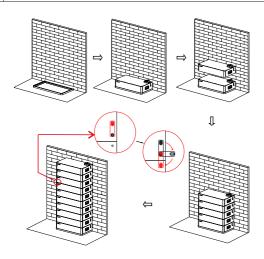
Installazione a pavimaneto di più Moduli Batteria AXE 5.0L con base.
